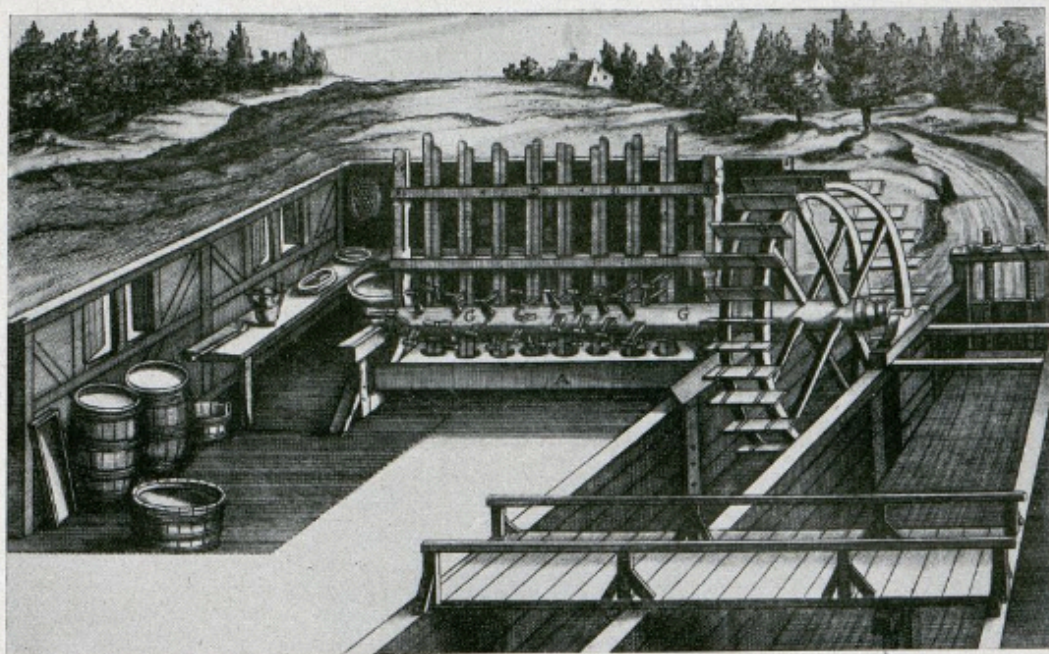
Pulverstampfe mit Wasserrad-Antrieb, 17. Jahrh.
